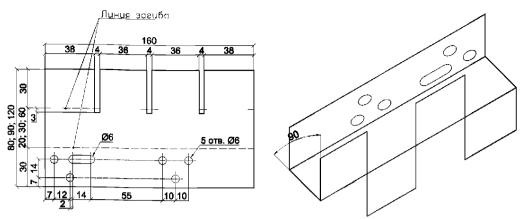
Анкер НЕОПОРМ для скрытого крепления теплоизоляции к стене
